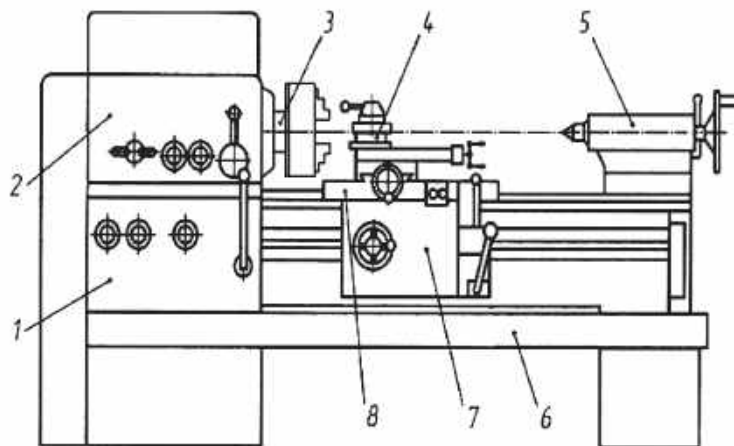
Схема токарно-гвинторізного верстата 16К20:
